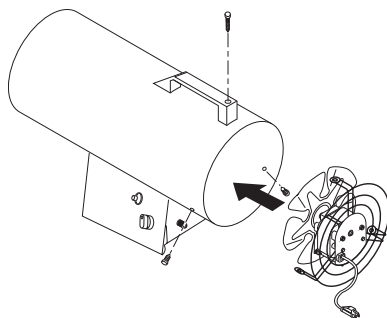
Installation du moteur et de la grille de protection du ventilateur dans l'appareil de chauffage
